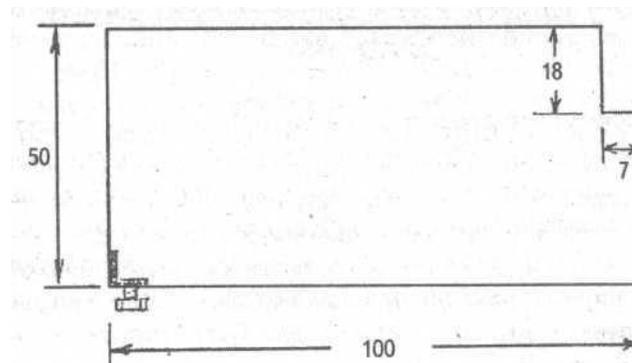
Приспособление для выборки шпунта и паза (вид с торца)
